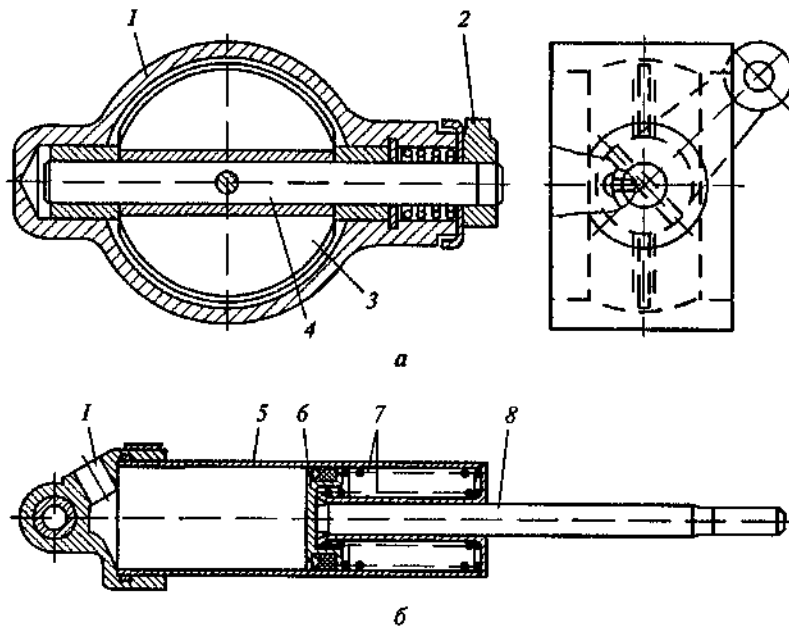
Моторный тормоз-замедлитель (а) и пневмоцилиндр (б) грузового автомобиля КамАЗ:
